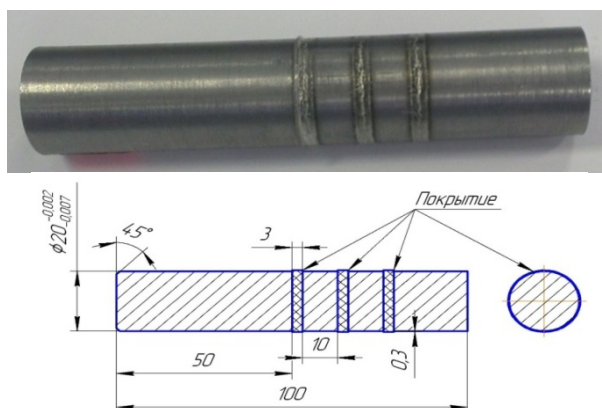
Образец с покрытием, полученным лазерной наплавкой
